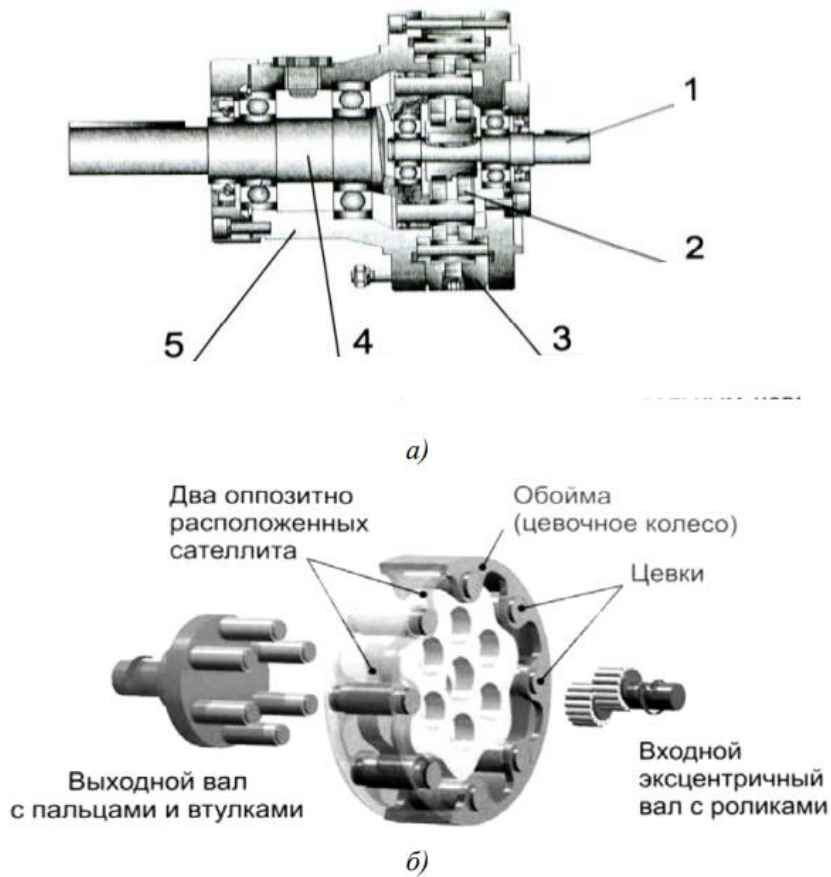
Конструкция циклоидального редуктора с двумя сателлитами и механизмом параллельных кривошипов
